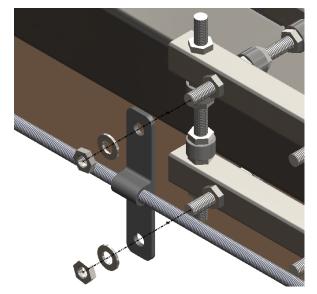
Detalle fijación varilla central al carro. Fuente: elaboración propia.
